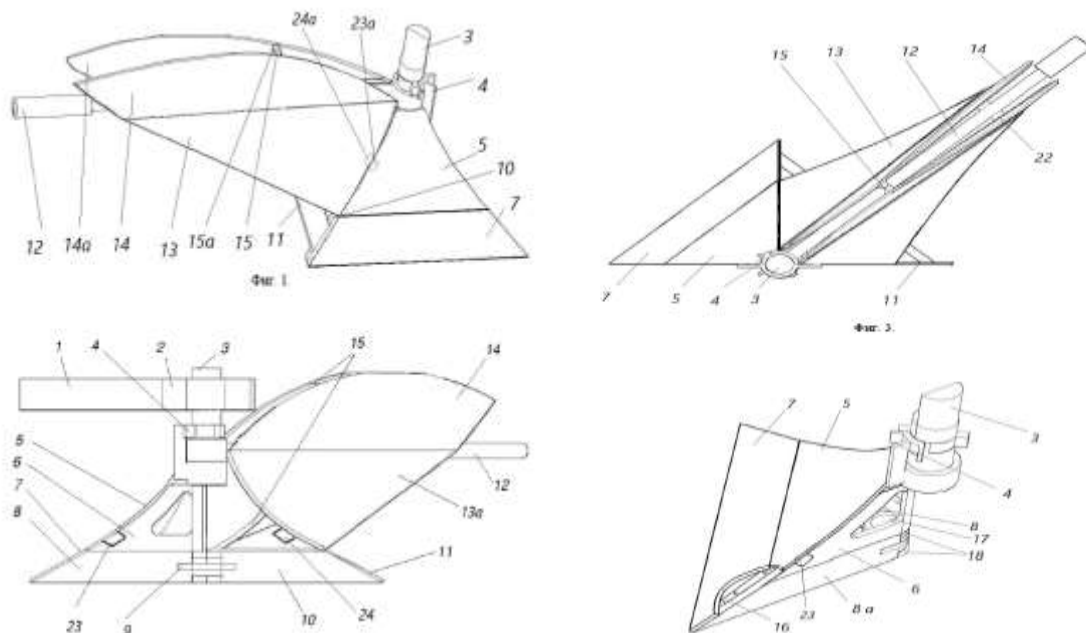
Поворотный плуг с опрокидывателями с геометрической комбинированной рабочей поверхностью.
